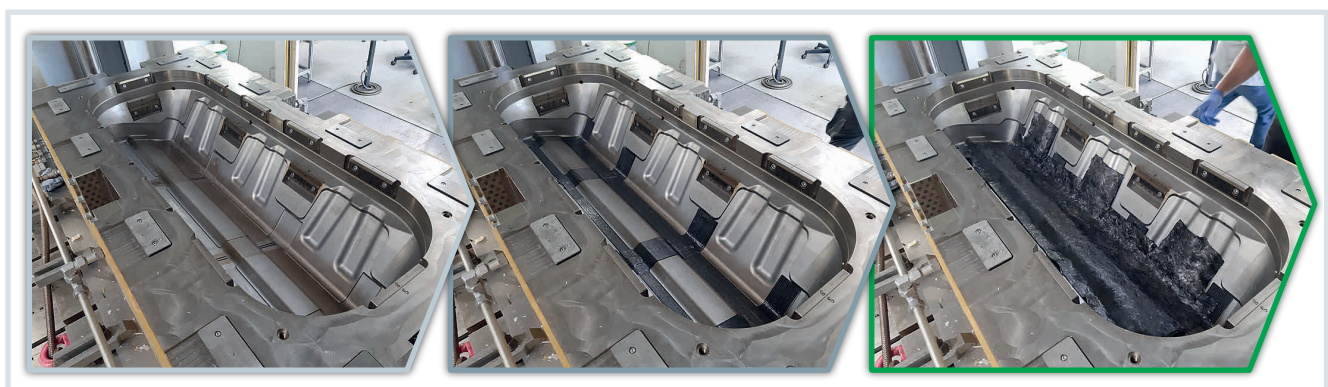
Untere Hälfte des Werkzeugs, in dem die äußere Sitzschale entsteht: geöffnetes Werkzeug, eingelegte lokale Verstärkung, im Werkzeug abgelegtes SMC-Material (von links). © Fraunhofer ICT
